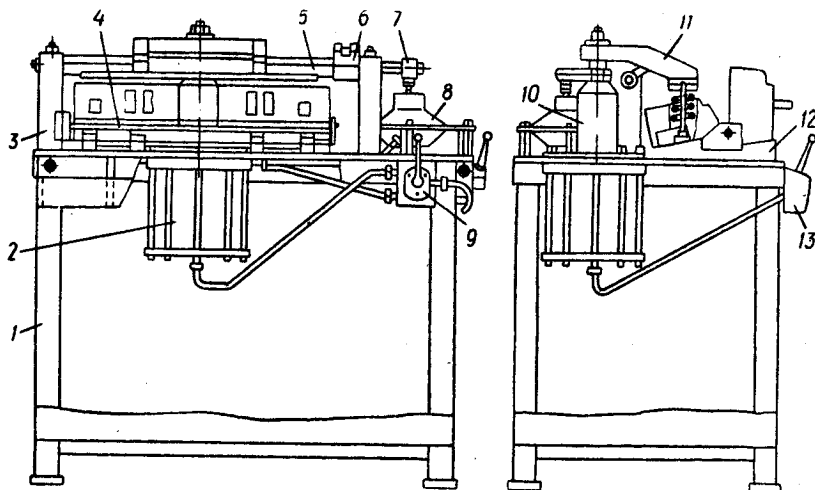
Стенд для розбирання і складання головок блока циліндрів:
